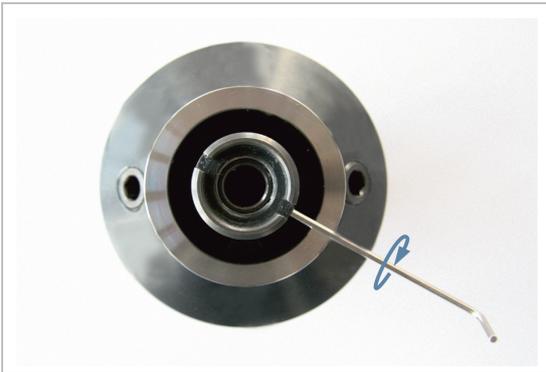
Gewindestift des Spannkopfes zuschrauben
